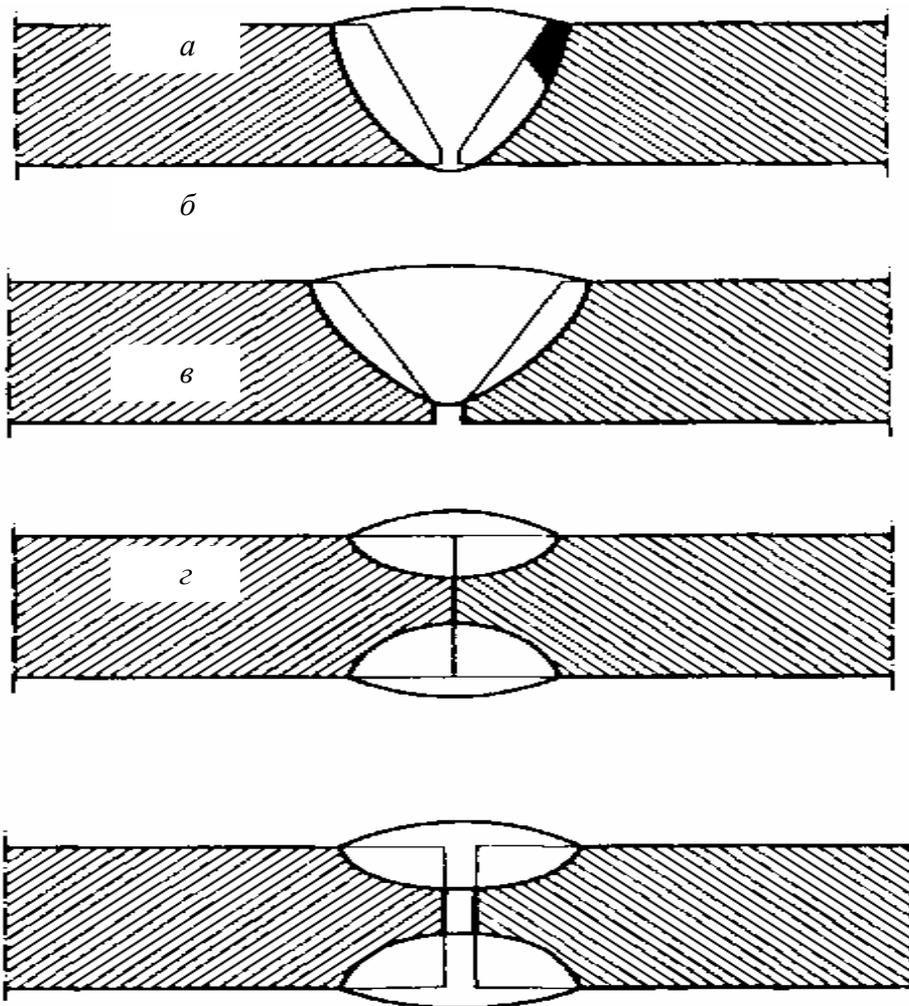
Непровар: *а* – односторонний основного металла; *б* – зоны подварки; *в* – двустороннего сварного шва; *г* – то же с зазором.
